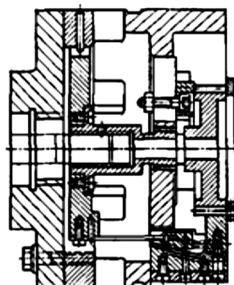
Патрон для установки и закрепления зубчатого колеса при шлифовании отверстия
